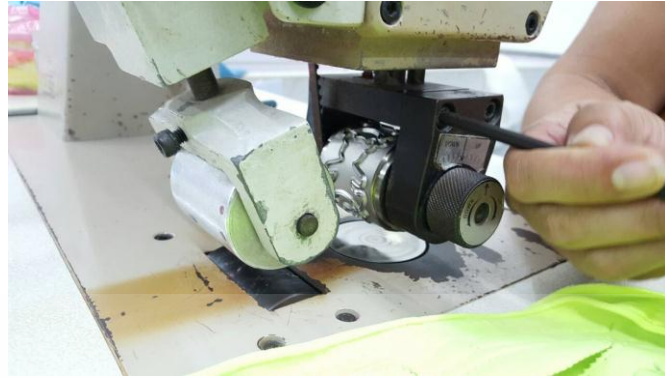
ภาพเครื่อง Ultra Sonic Sewing Machine
